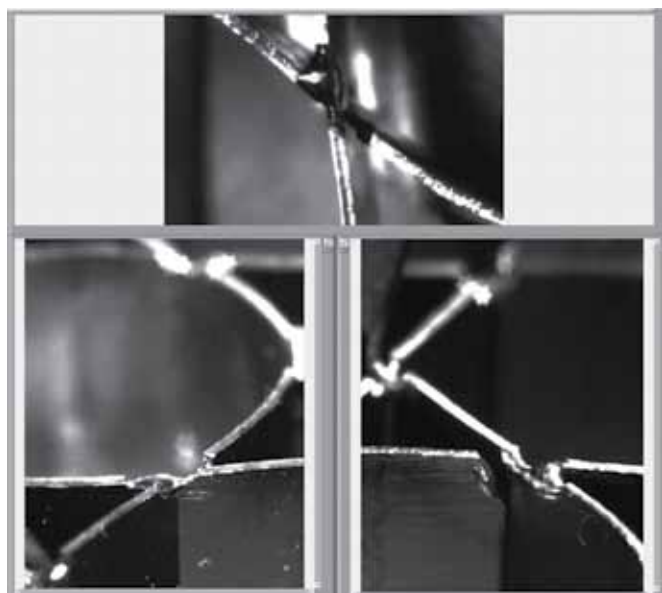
Комбинация изображений одного сварного соединения с разных камер
